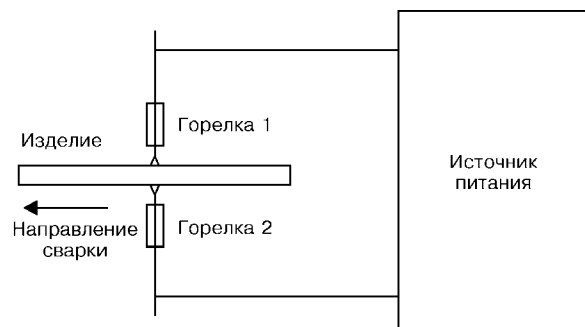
Схема двухсторонней дуговой сварки
